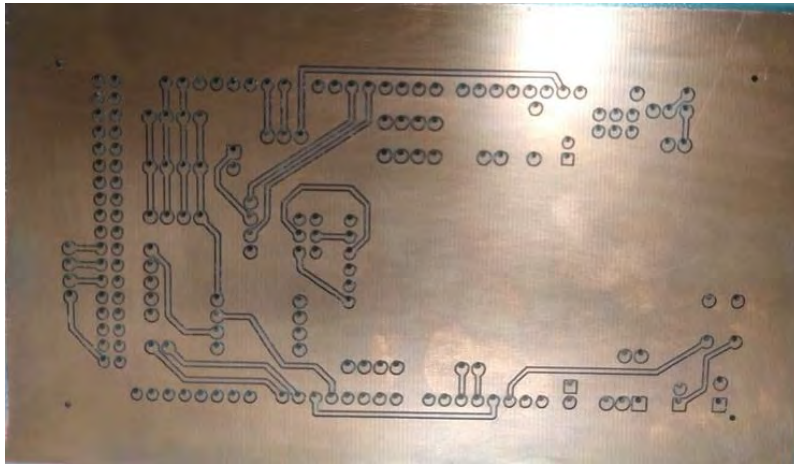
Prueba experimental de maquina no calibrada PCB de doble cara
